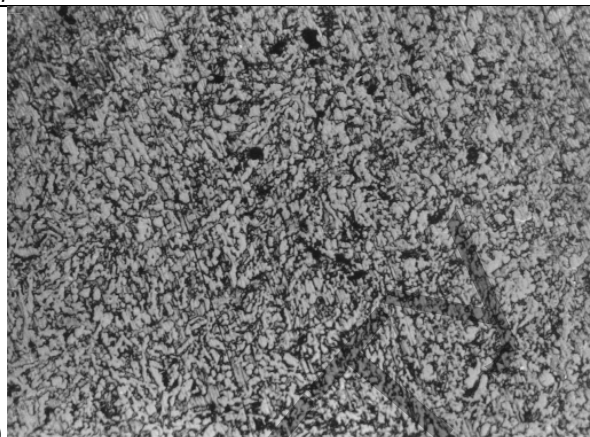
Хрупкий камневидный излом высокобористой наплавки
